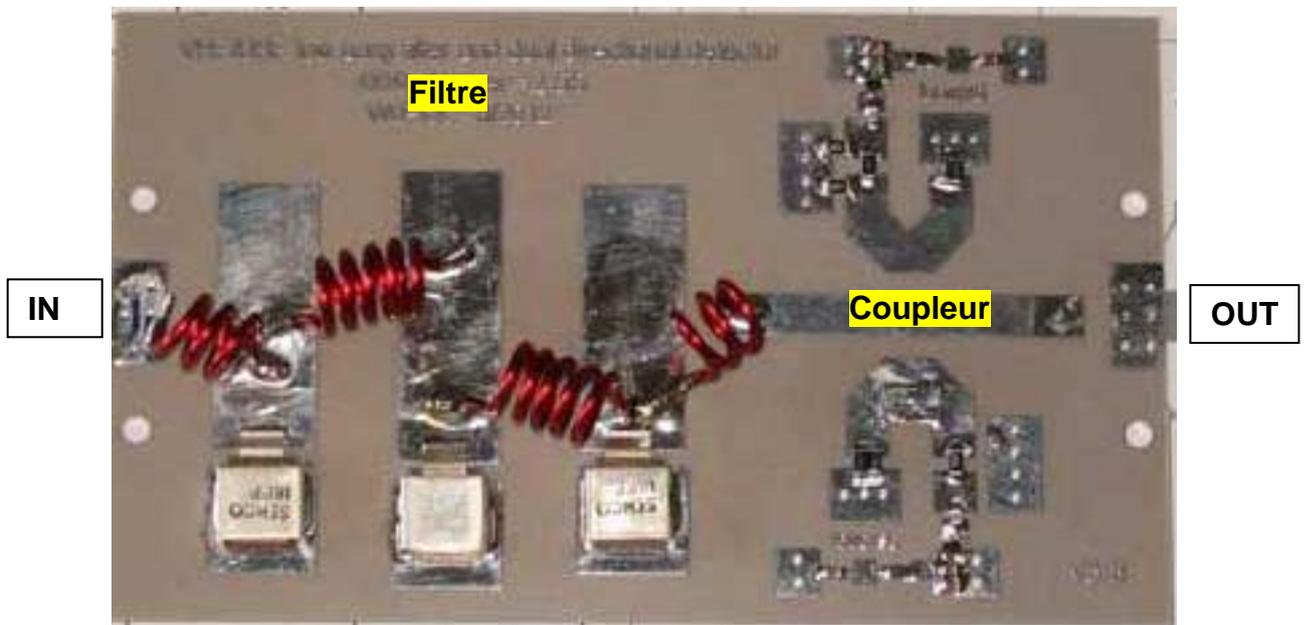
PCB du filtre passe-bas avec coupleur directionnel
